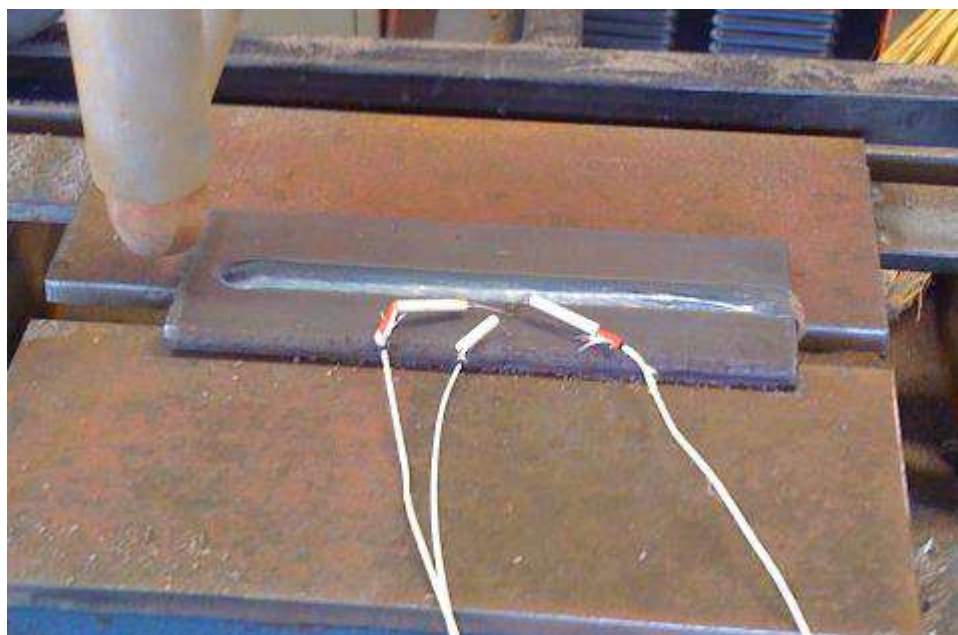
Chapa com o cordão de solda mostrando a fixação dos termopares.
